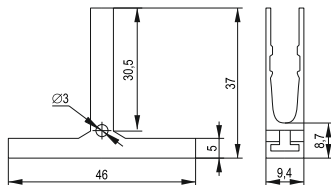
Габаритные и установочные размеры держателя маркировки
